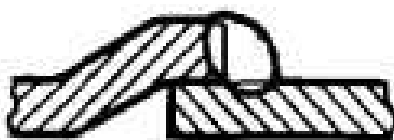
Сварное раструбное соединение труб [2]
